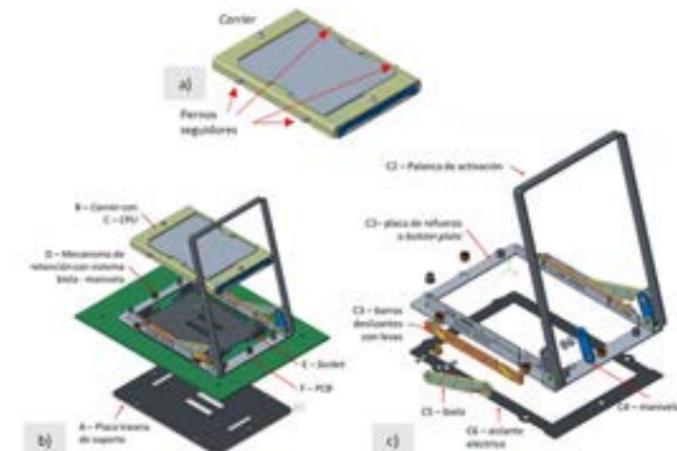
a) Vista explosionada del mecanismo de retención y b) vista explosionada del bolster plate.
